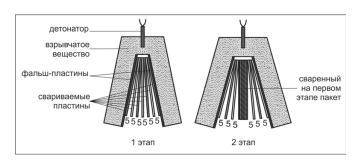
Схема сварки пластин за два этапа. Цифрами обозначены зазоры между пластинами
